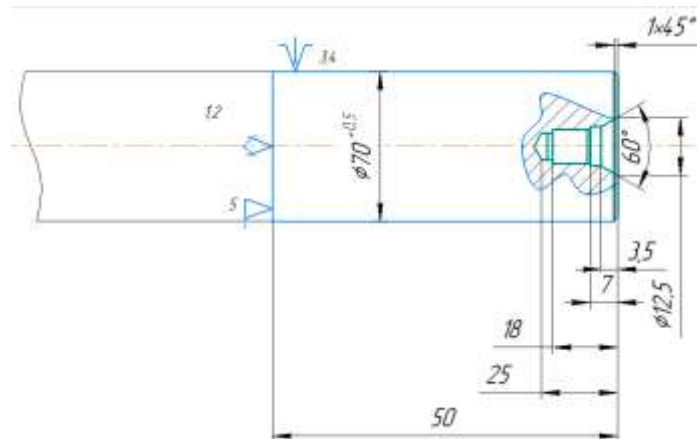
Базування та закріплення заготовки на операції 010.
